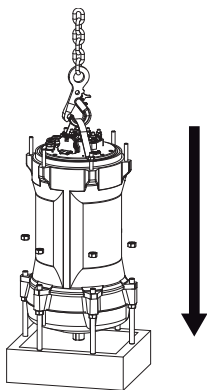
Монтаж корпуса двигателя (J 205, J 405)
